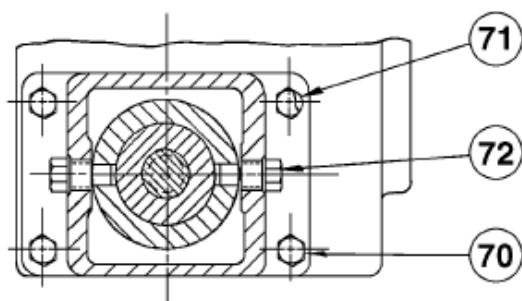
Деталировочный чертеж кронштейна маховика. Приводы размера В и С
